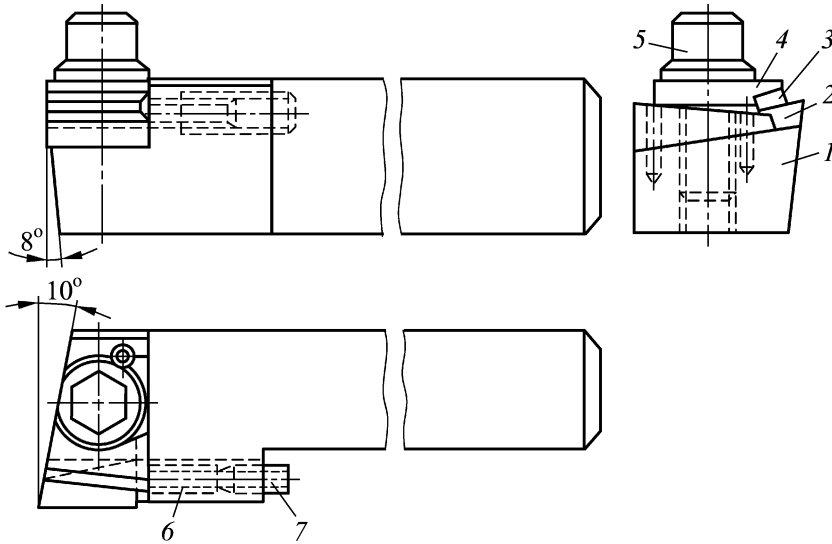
Резец с креплением пластины прижимной планкой:
